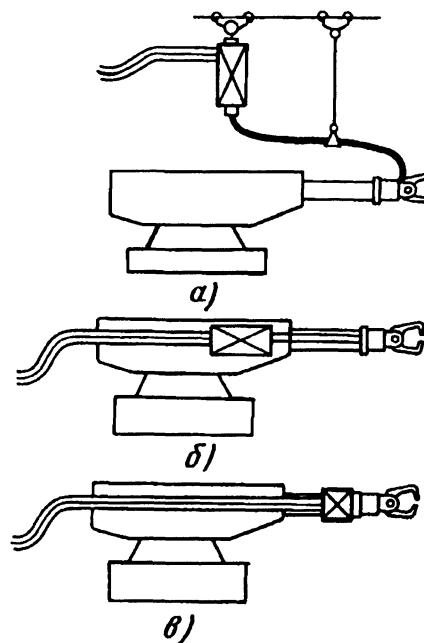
Размещение сварочного трансформатора при роботизированной контактной точечной сварке
